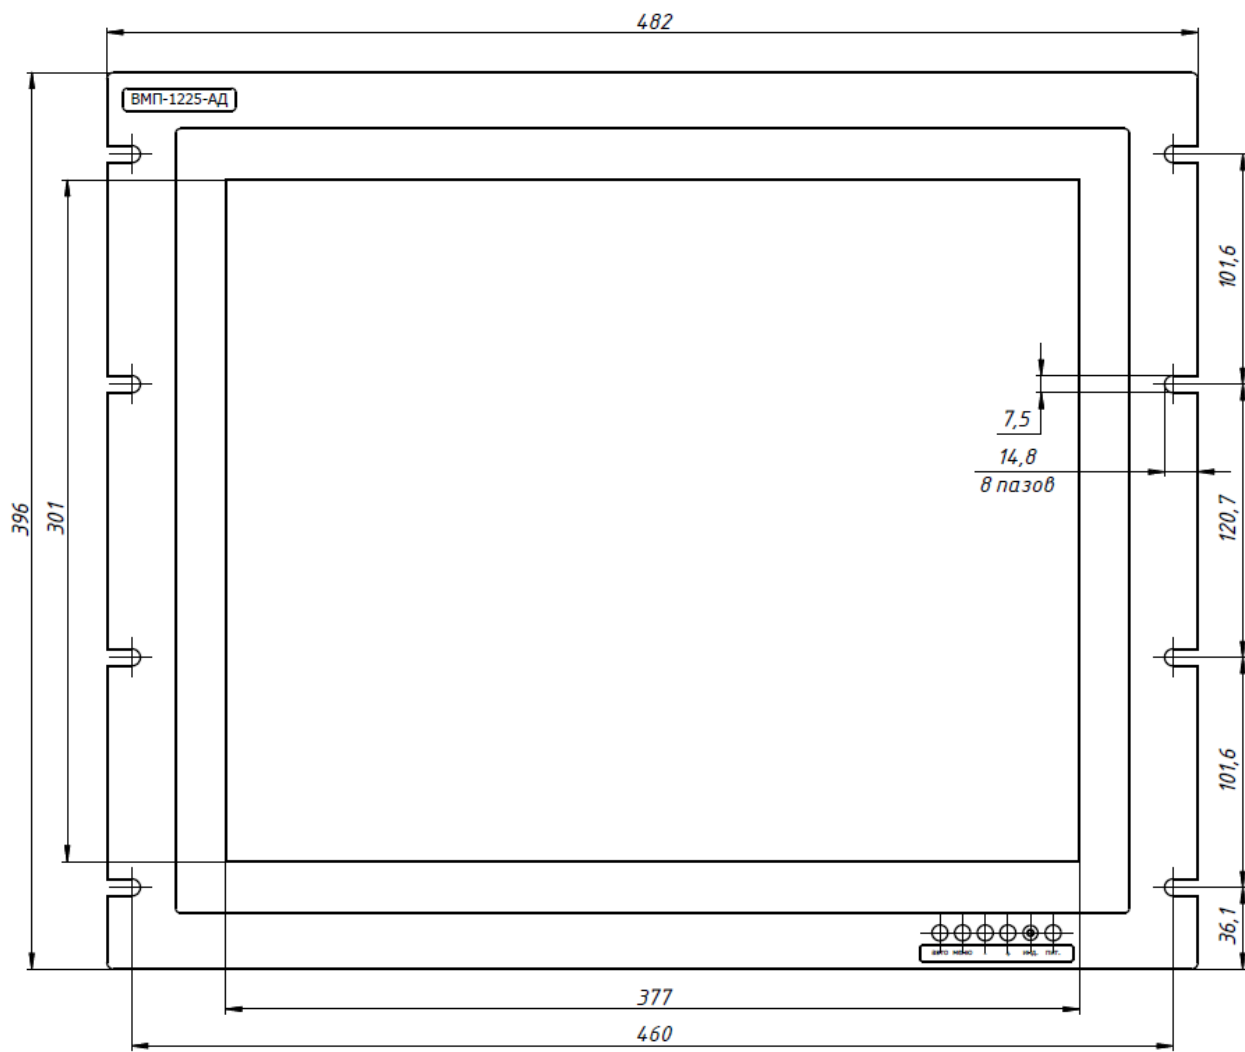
Габаритный чертёж видеомонитора в исполнении ВМП1225-АД-4-Х-Х-Х, вид спереди
